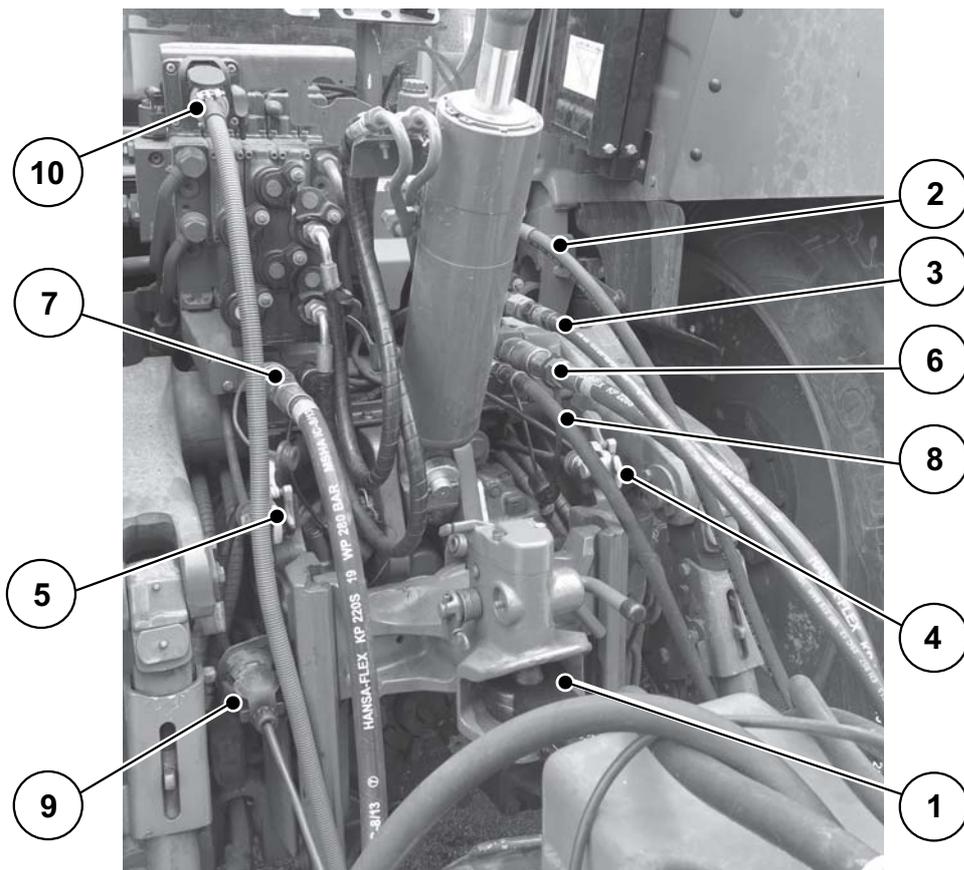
Anschlussreihenfolge Überladewagen TWS-H-7010
